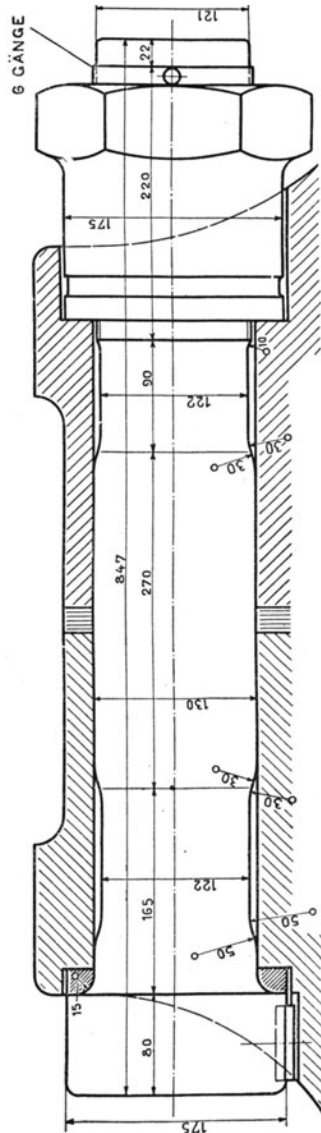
Werkstattzeichnung eines Schraubenbolzens.
